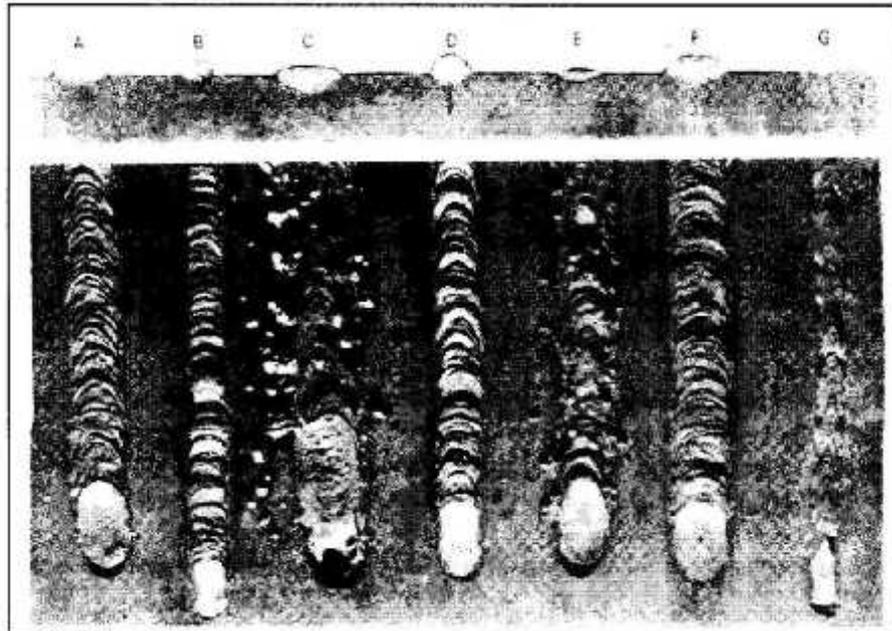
Efecto de los principales parámetros de soldeo en el cordón.
